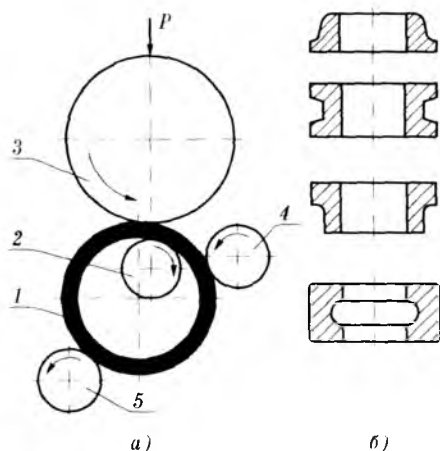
Схема раскатки (а) и формы раскатанных заготовок (б):
